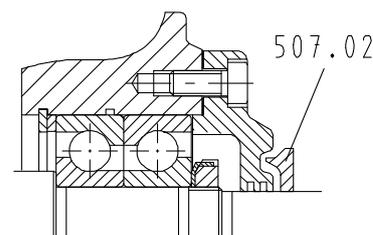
Сборочный чертеж исполнения подшипникового кронштейна P02 - P06
